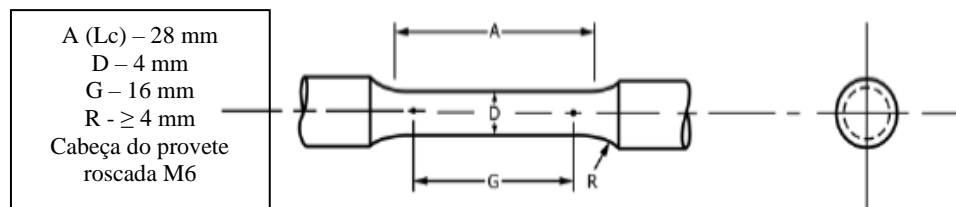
Provette cilíndrico de dimensões pequenas. Adaptado de (ASTM E8/E8M, 2022).
